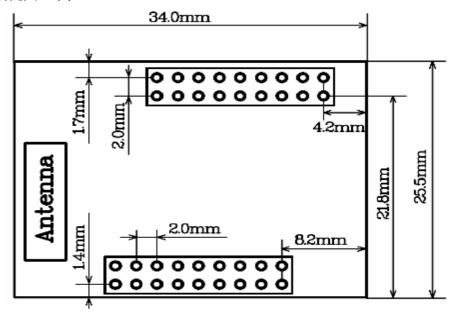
GC-06 (GC-04-DIP) 外形尺寸 (顶视图)
